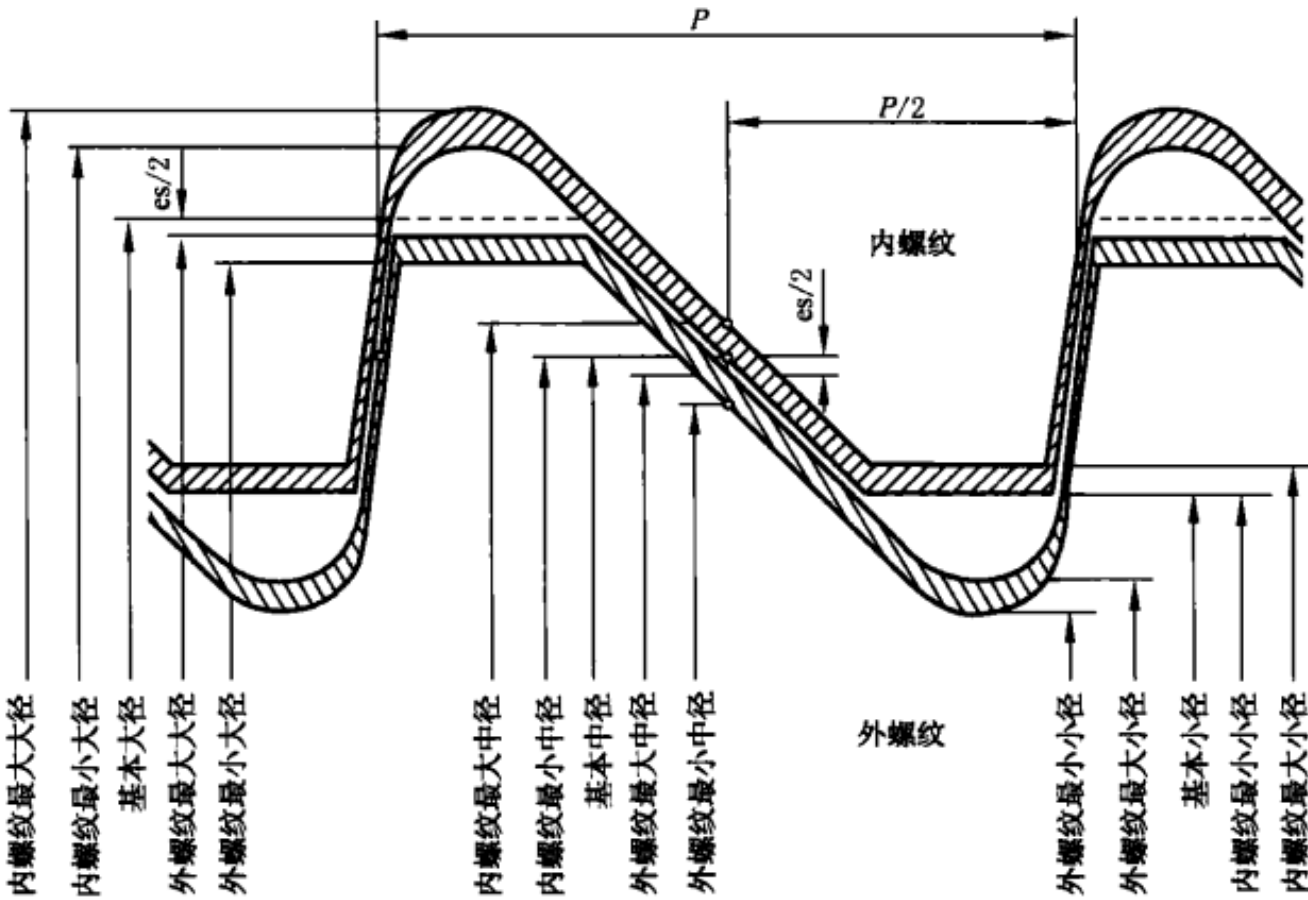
美制锯齿形螺纹的公差带位置
